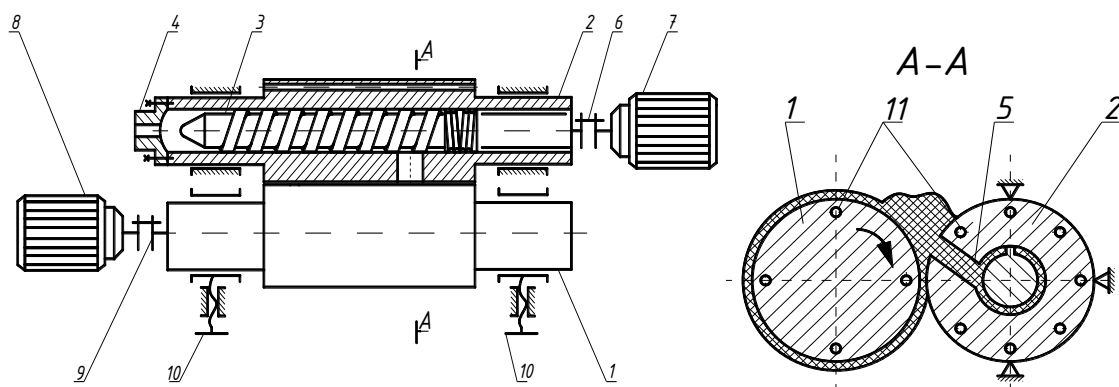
Валково-шнековый агрегат: 1-передний валок; 2-задний неподвижный валок; 3-шнек; 4- формирующая головка; 5- загрузочное окно; 6,9- муфта; 7,8-мотор-редуктора; 10 - регулирующее устройство; 11- электронагреватели.
